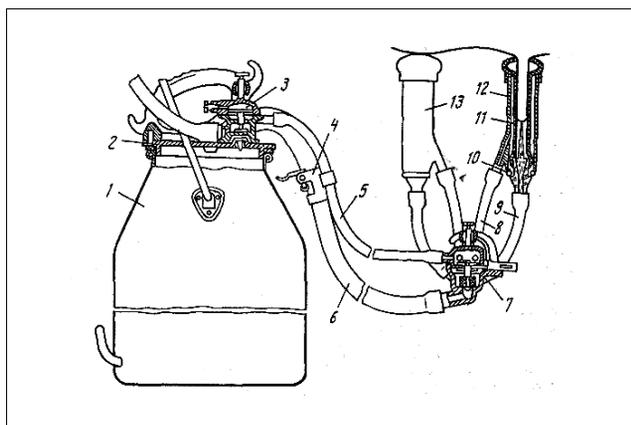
Трехтактная доильная машина ДА-3 (автор В.Ф. Королев): 1 – доильное ведро; 2 – крышка ведра; 3 – пульсатор; 4 – зажим молочного шланга; 5 – воздушный шланг; 6 – молочный шланг; 7 – коллектор; 8 – вакуумный патрубкок; 9 – молочный патрубкок; 10 – соединительное кольцо; 11 – сосковая резина; 12 – гильза стакана; 13 – доильные стаканы
